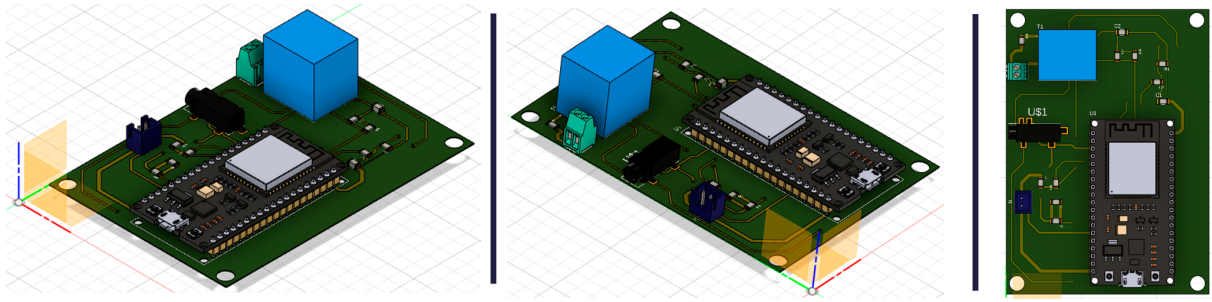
Vistas del diseño en 3D de izquierda a derecha a) vista superior izquierda b) vista superior derecha c) vista superior Fuente Autor
